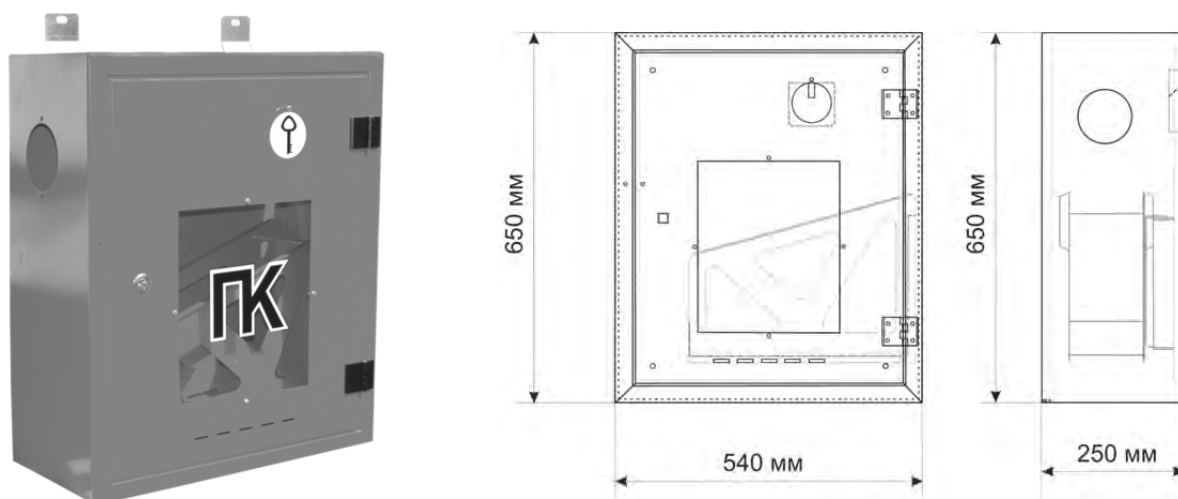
Внешний вид и габаритные размеры ШПК
